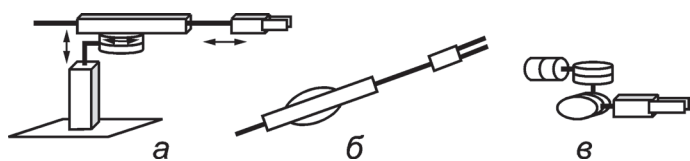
Схема робота, работающего в цилиндрической системе координат:
